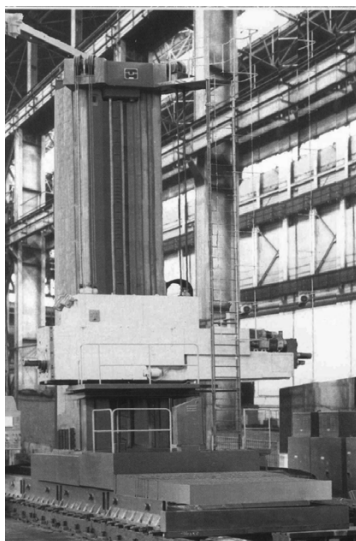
Тяжелый многоцелевой станок сверлильно-фрезерно-расточной группы
